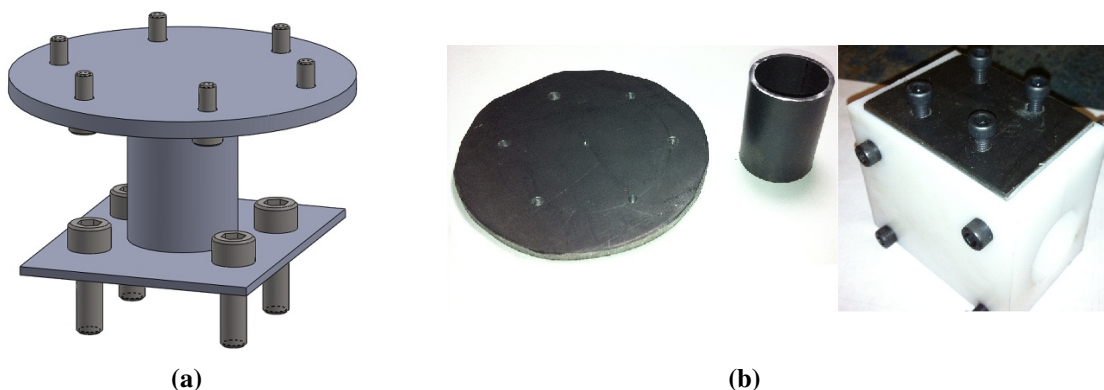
Diseño y construcción de la extensión para la brida del robot. a) Diseño en CAD. b) Fabricación.
